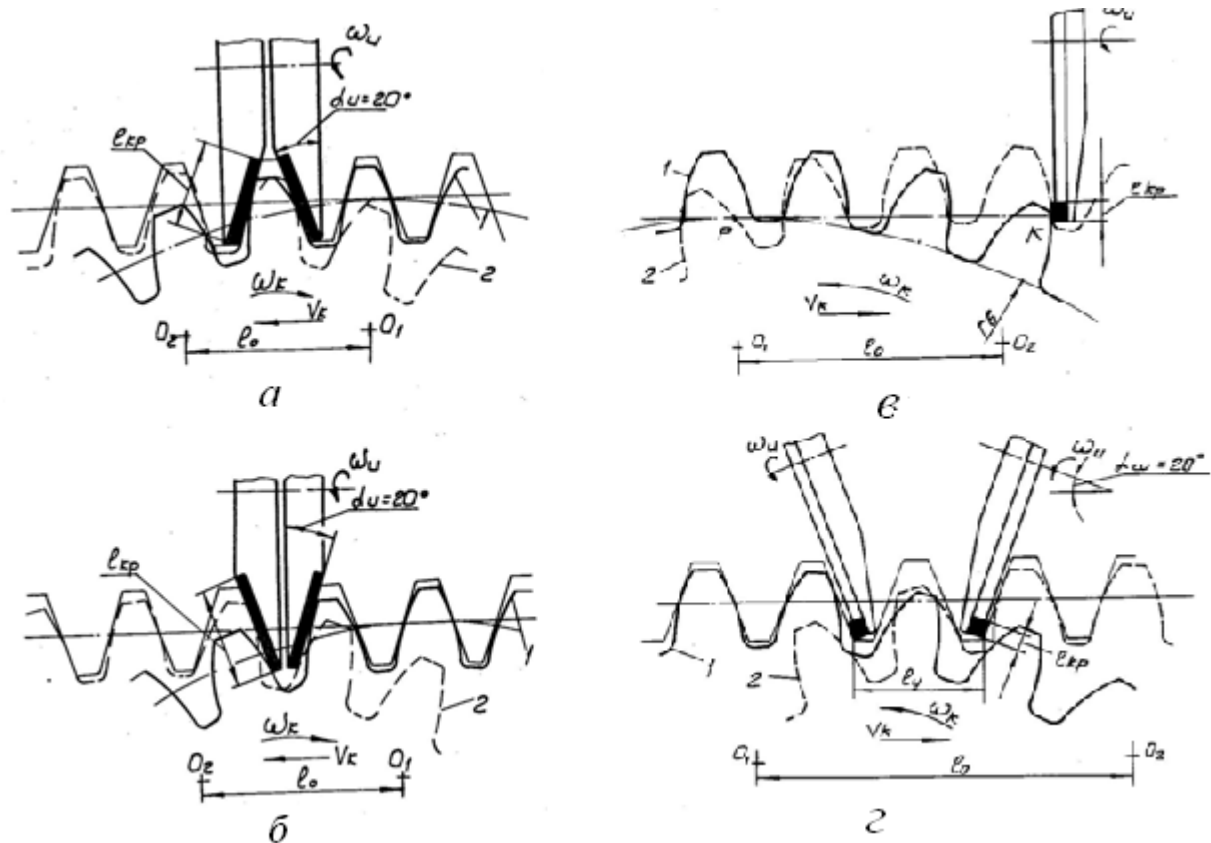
Перспективні технологічні схеми швидкісного зубофрезерування дисковими немодульними фрезами: а - схема різання I; б - схема різання II; в - схема різання III; г - схема різання IV
